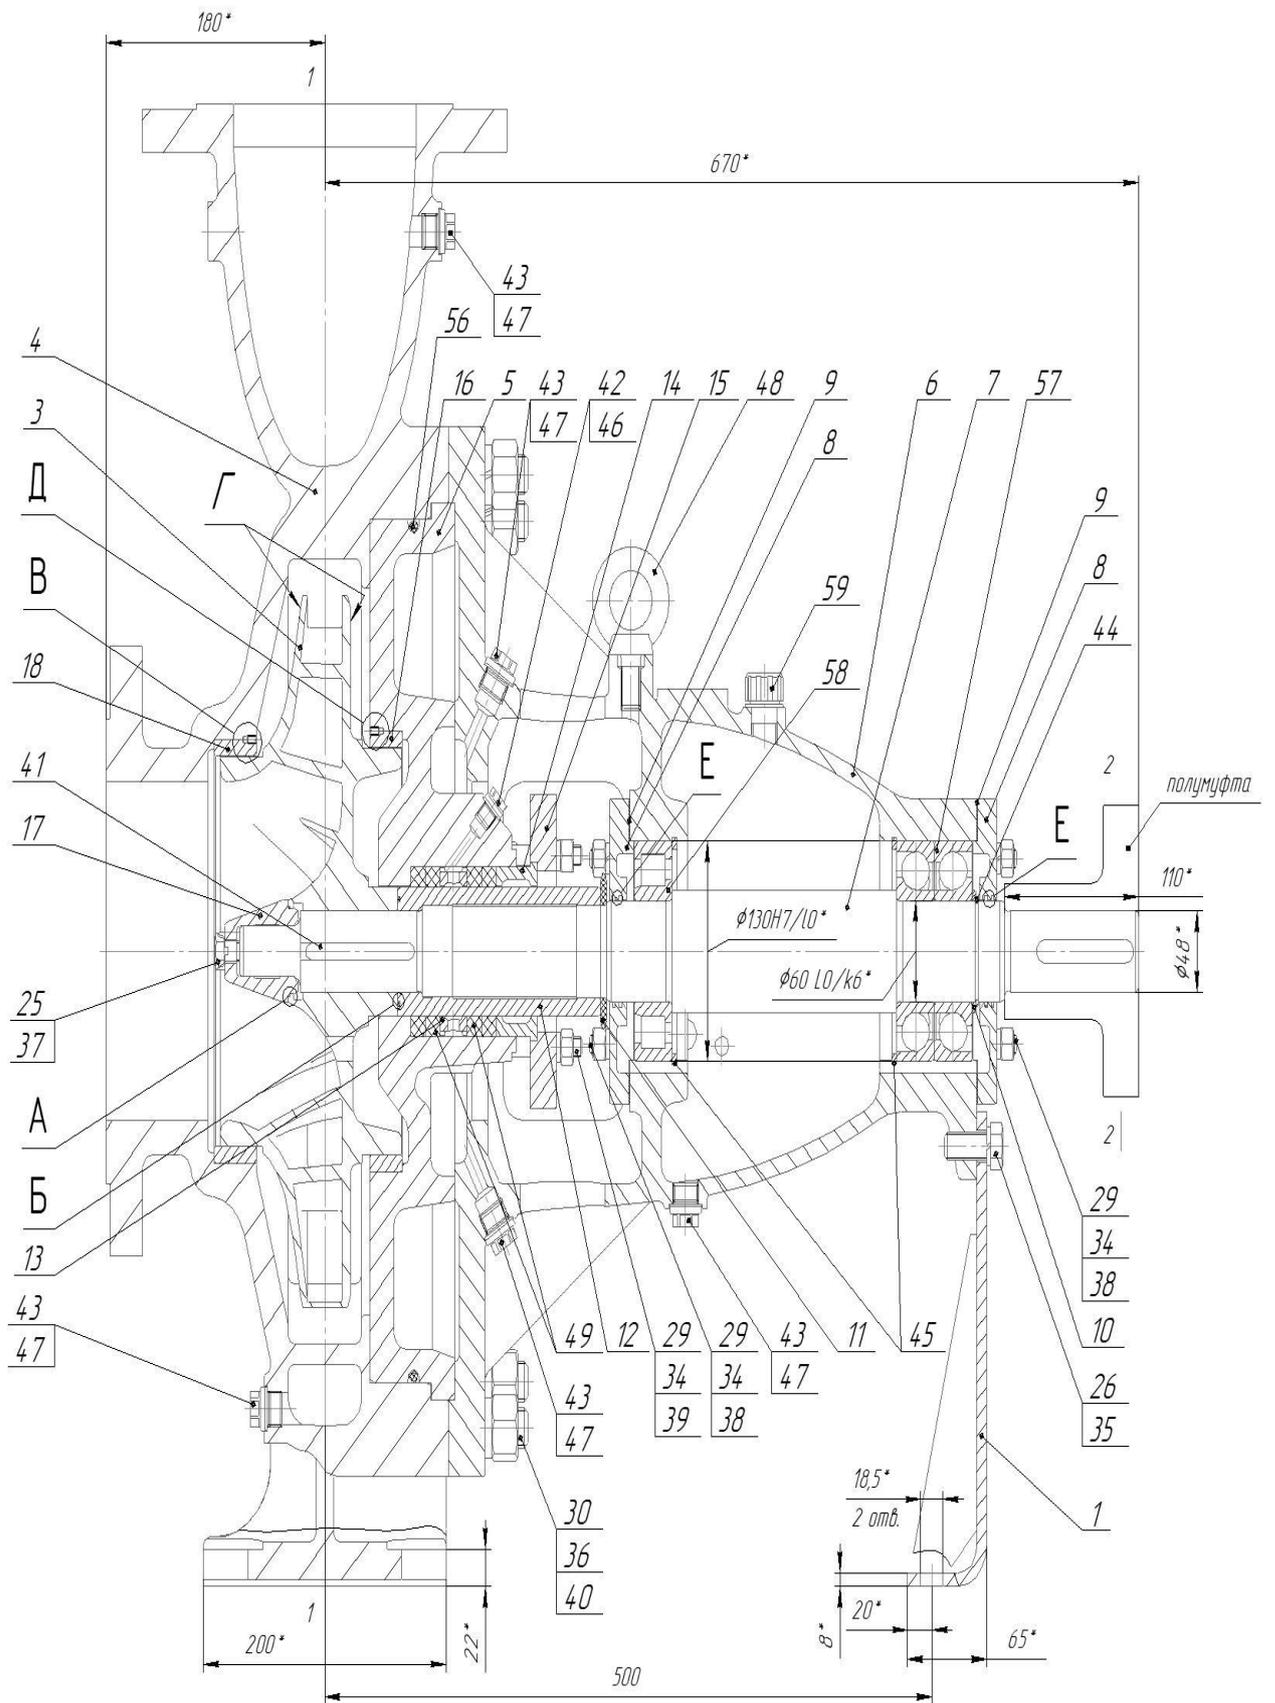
Чертеж центробежного консольного насоса СНР 150-500. Часто износ вала возникает в контакте с деталью рабочее колесо поз.3, втулка упорная поз.12 , также подшипники 57,58 в случаях подшипники просто заменяют
